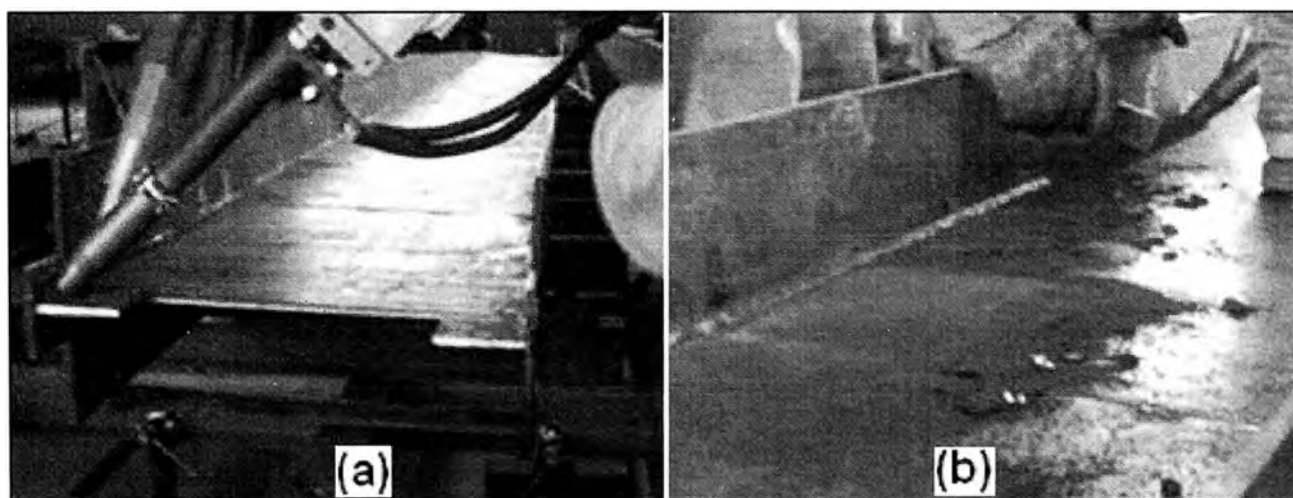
Soldadura del primer cordón con SAW.
